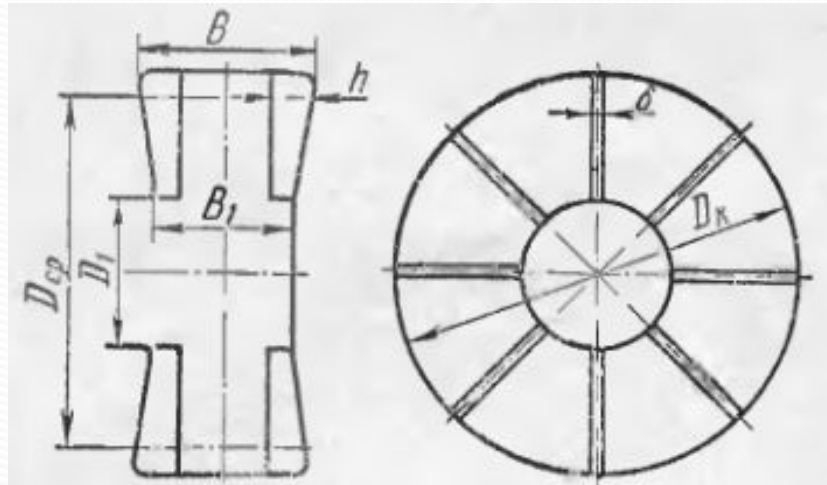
Геометрия корпусов № 1; 1а; 1б; 2; 2а; 2б
